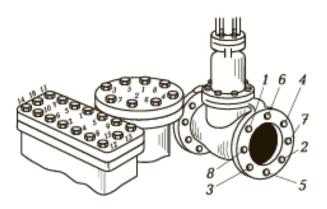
Порядок затягивания резьбовых соединений (указан цифрами 1—16)
